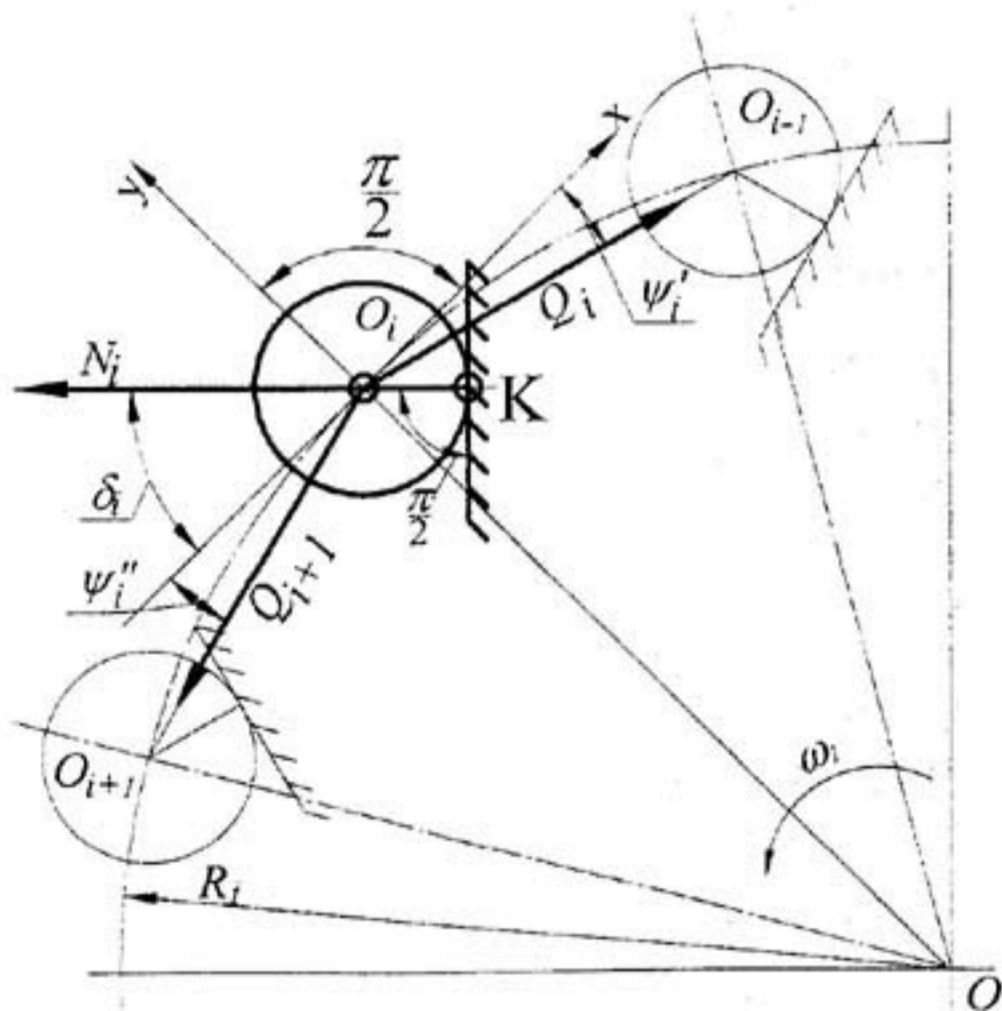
Параметры зацепления i -го шарнира с зубом звездочки
